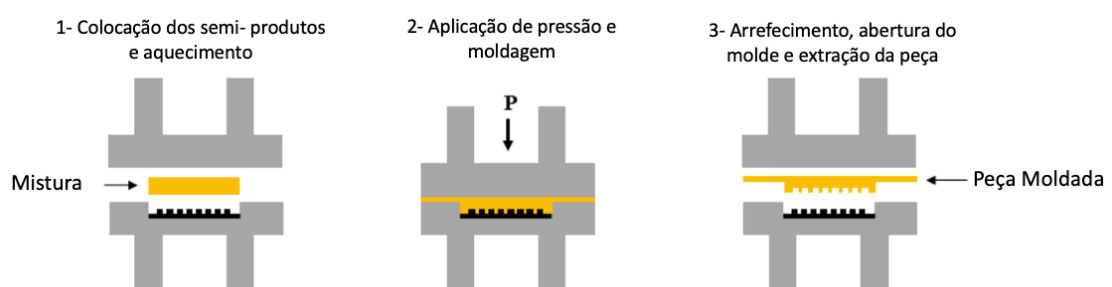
Processo de Moldação por Compressão a Quente, adaptado de [33]
